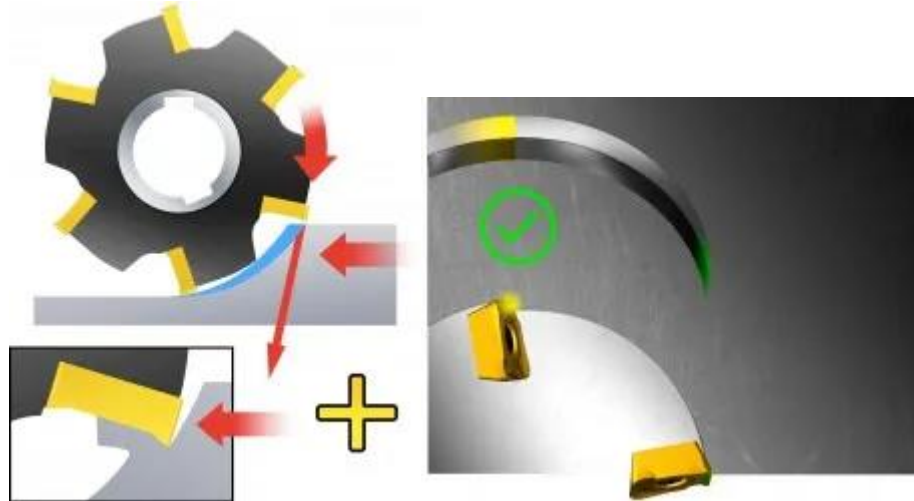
Попутне фрезерування, утворення стружки
